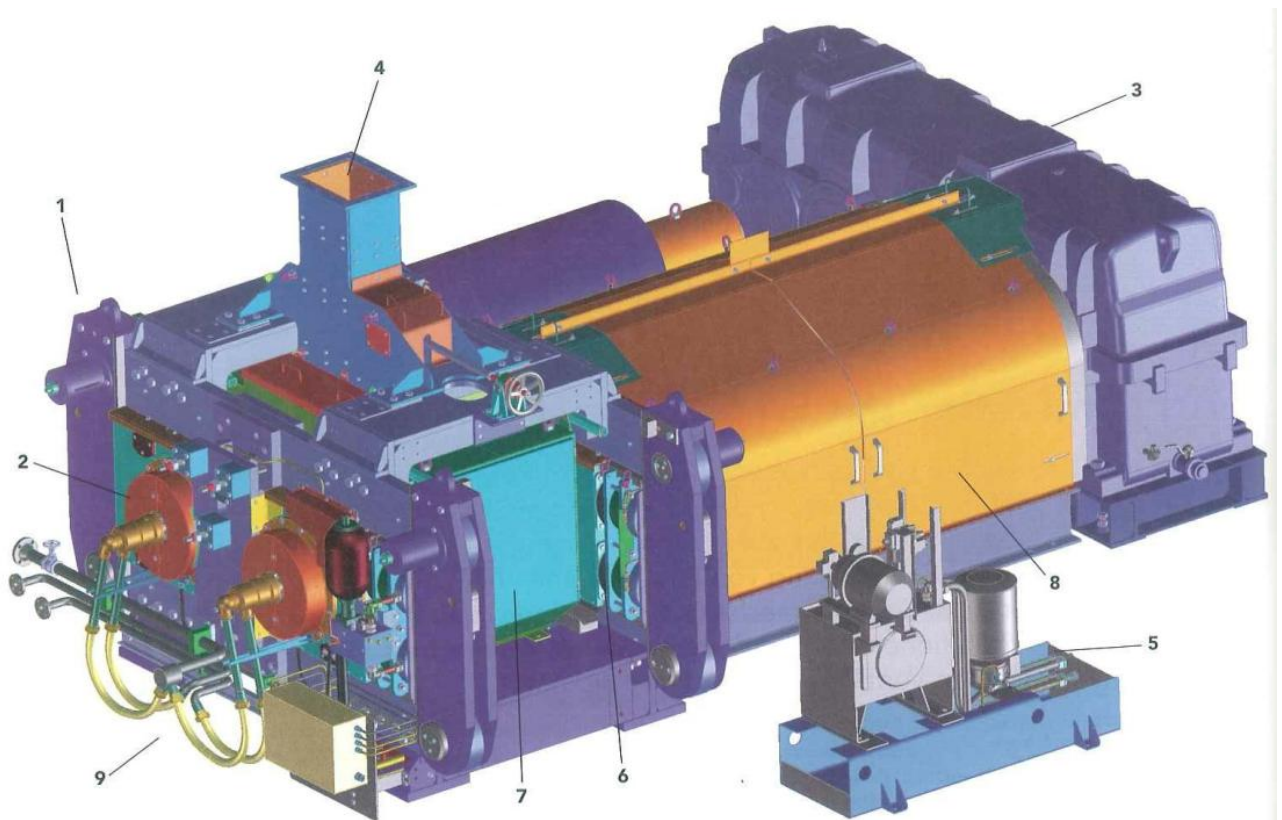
Валковий прес для брикетування (загальний вигляд).
